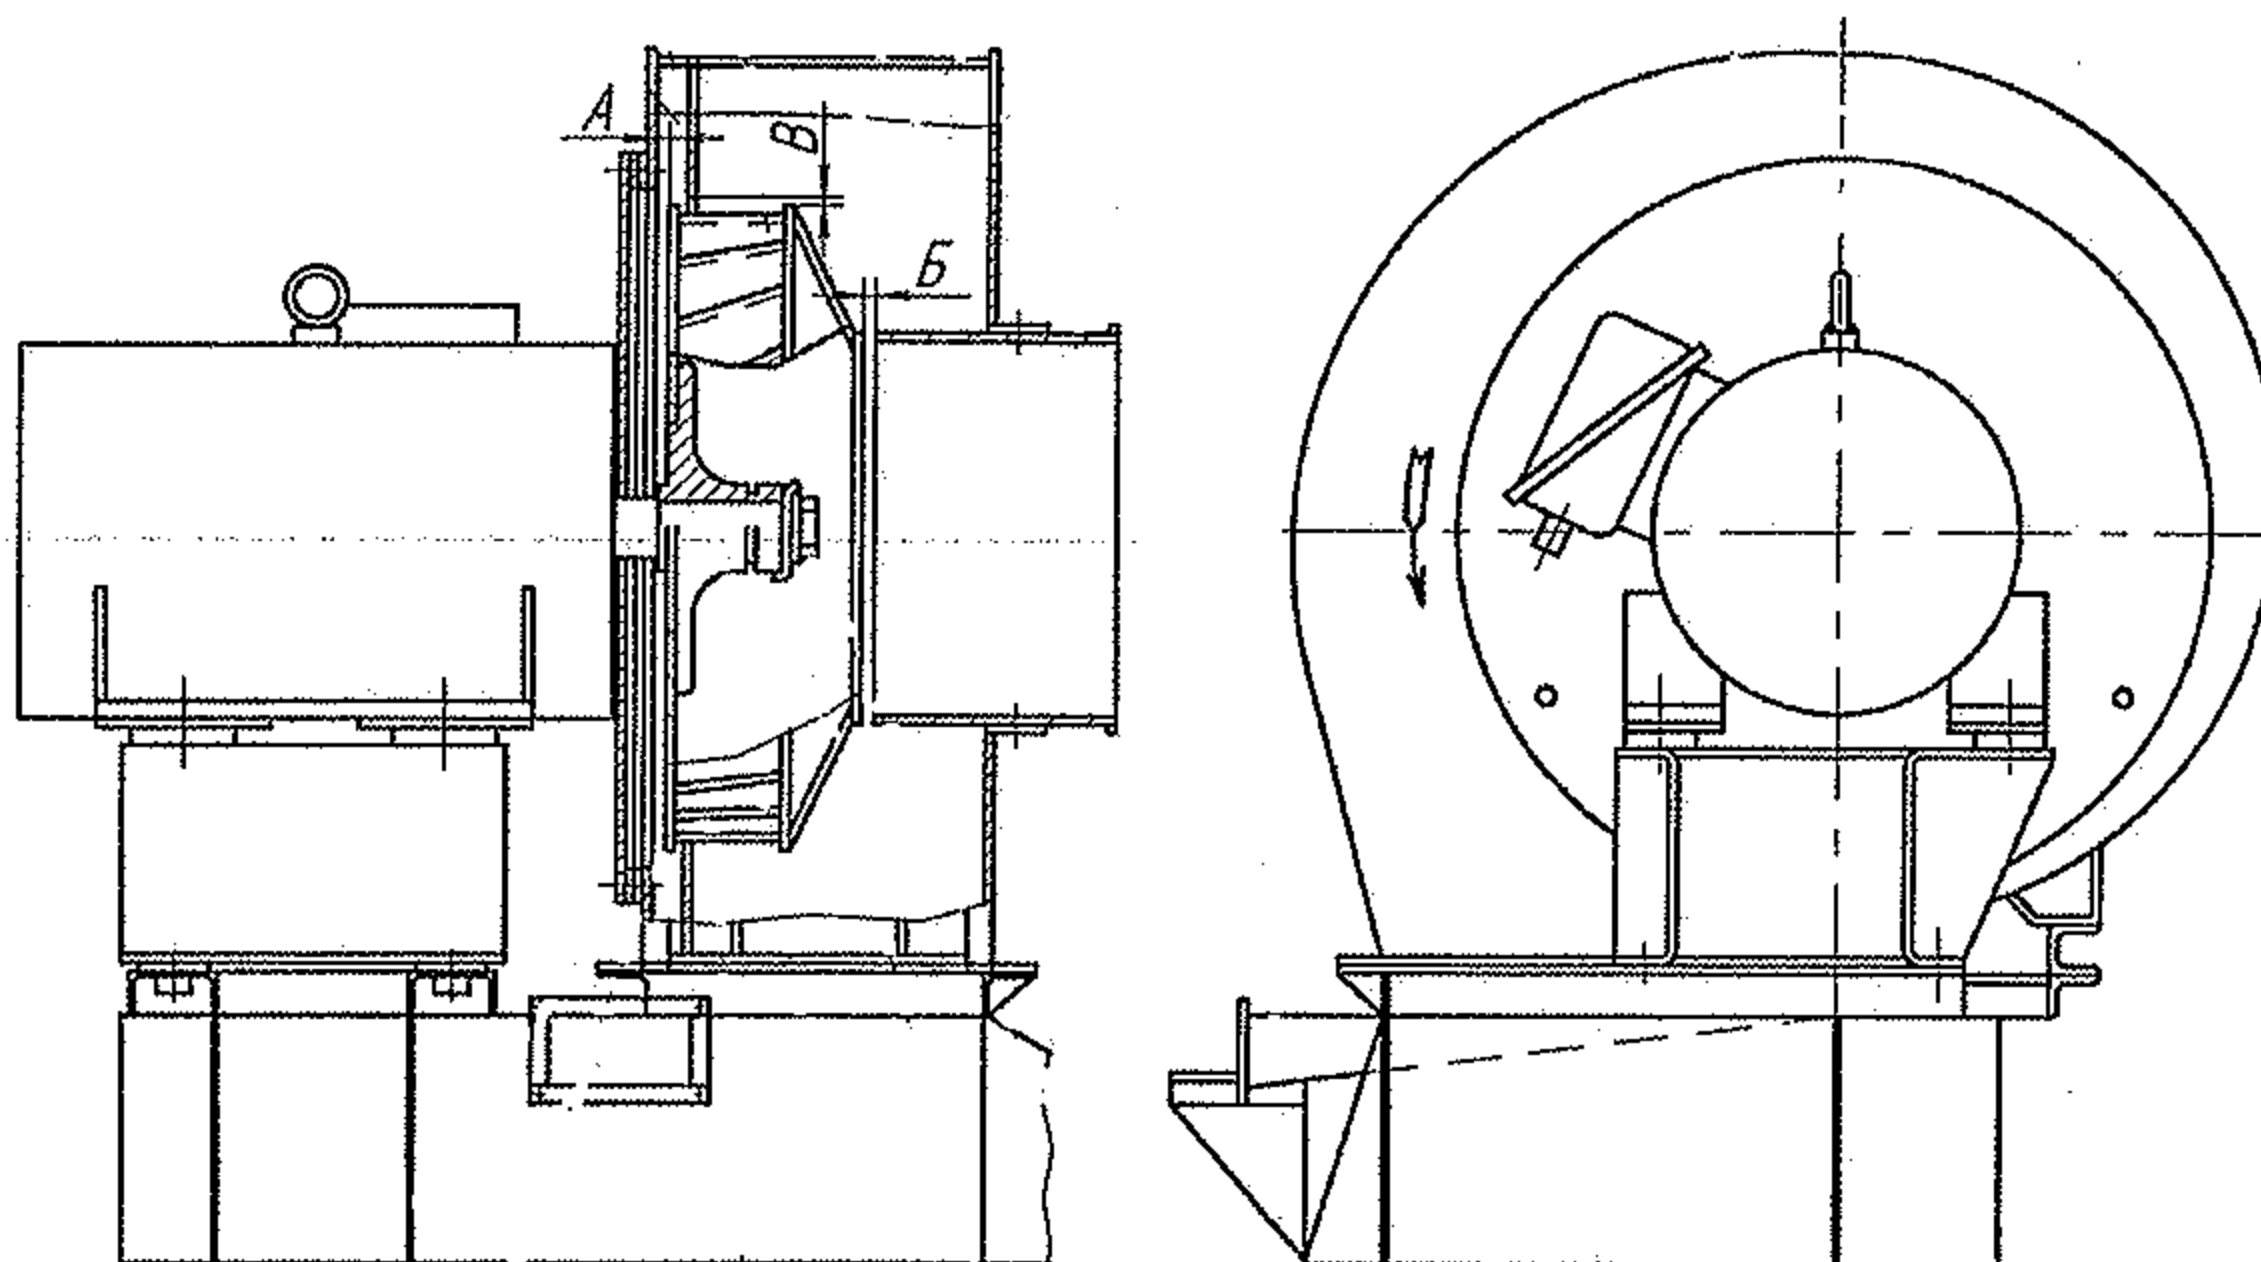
Блок центробежного вентилятора-воздухоочистителя ЦВ9-37,6-7,6
